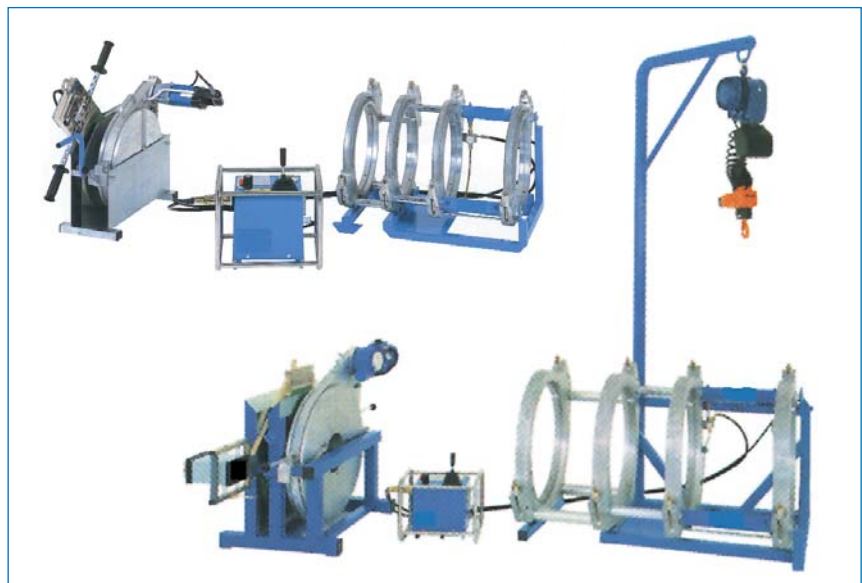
Heizelementstumpfschweißmaschinen für Rohre d90 – d315 und d355 – d630
